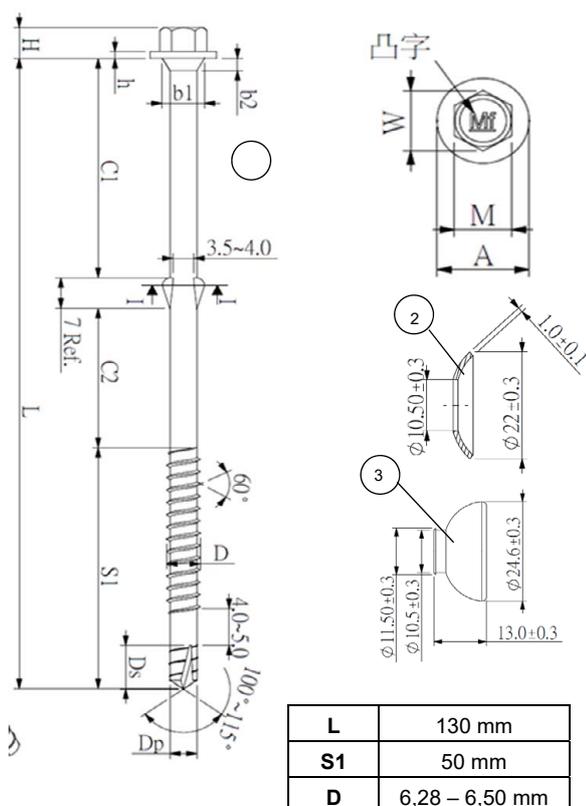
Shen Fung Spezialbohrschraube 6,5 x 130 mm
